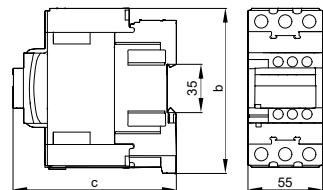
Габаритные размеры контакторов КМИ-А-34012, КМИ-А-35012 / Figure 3 — Overall dimensions of contactors KMI-A-34012, KMI-A-35012
